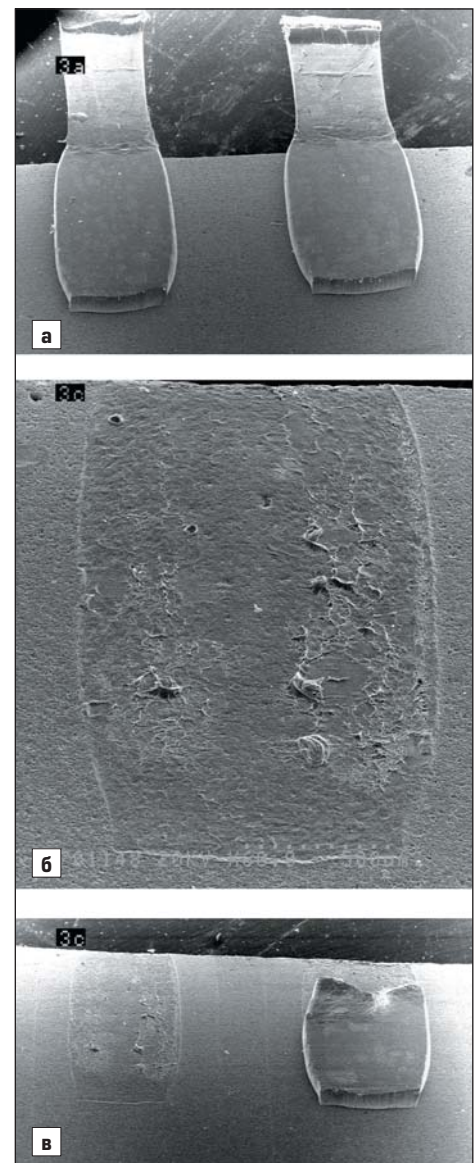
Внешний вид соединения вывода с напыленным слоем алюминия: а) после термокомпрессионной сварки; б) после проверки прочности на отрыв; в) отслоение сварного соединения
